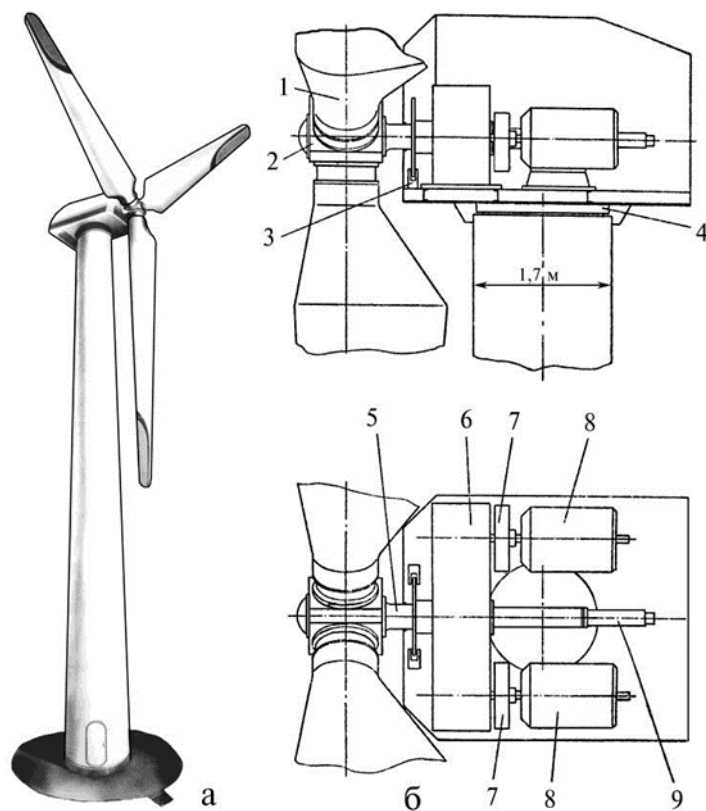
Агрегат вітроелектричний АВЕ-500: а – загальний вигляд; б – вміст головки агрегату: 1 – лопать; 2 – ступиця; 3 – гальмо вітроколеса; 4 – поворотний круг; 5 – вал; 6 – редуктор; 7 – гальмовий пристрій; 8 – генератор; 9 – пристрій повертання лопатей
